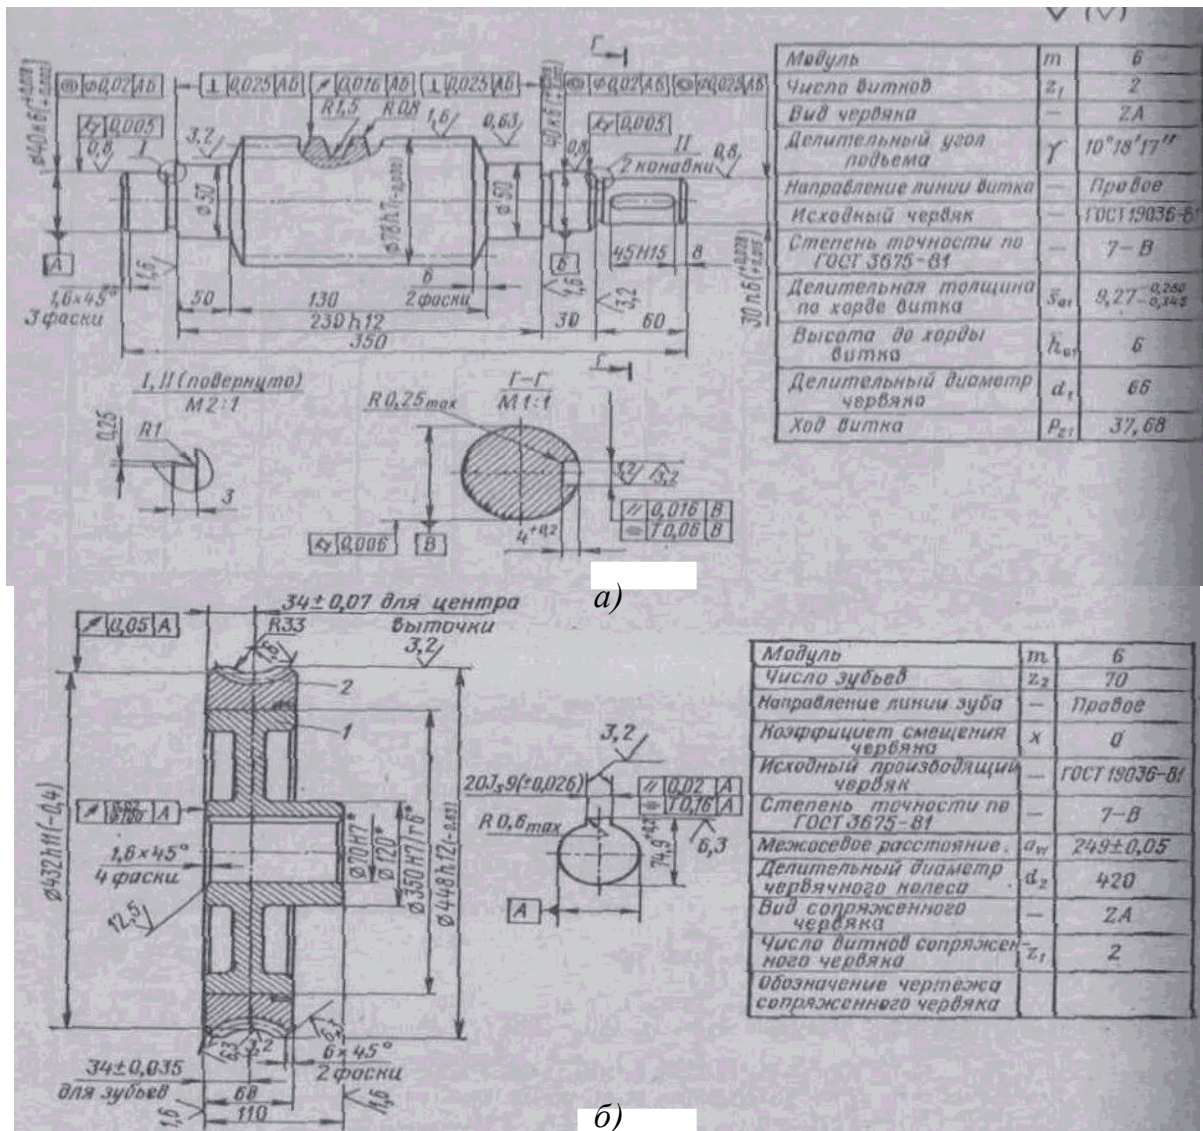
Рабочие чертежи деталей червячных передач: а – червяка-вала; б – червячного колеса
